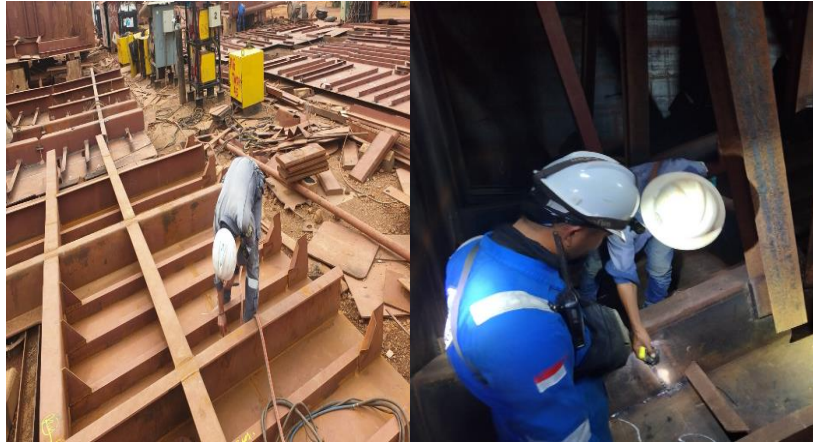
254. Visual Welding Inspection and Penetrant Test
